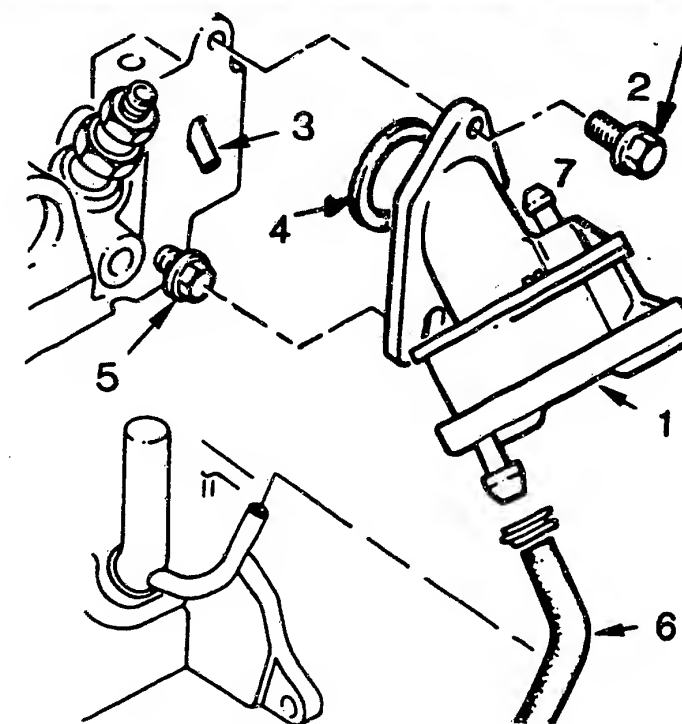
Diesel-Motor: 1 Vakuumpumpe am Zylinderkopf – 2. obere Befestigung – 3 Stößel – 4 O-Ring – 5 untere Befestigung – 6 Ölrücklaufschlauch – 7 Unterdruckanschluss.
